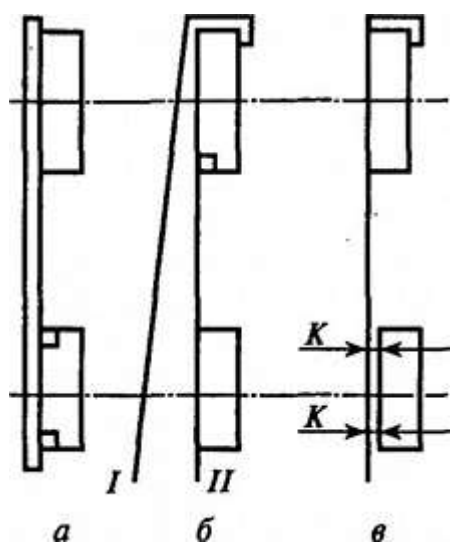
Схемы проверки установки шкивов на валы с помощью линейки (а) и шнуров (б,
